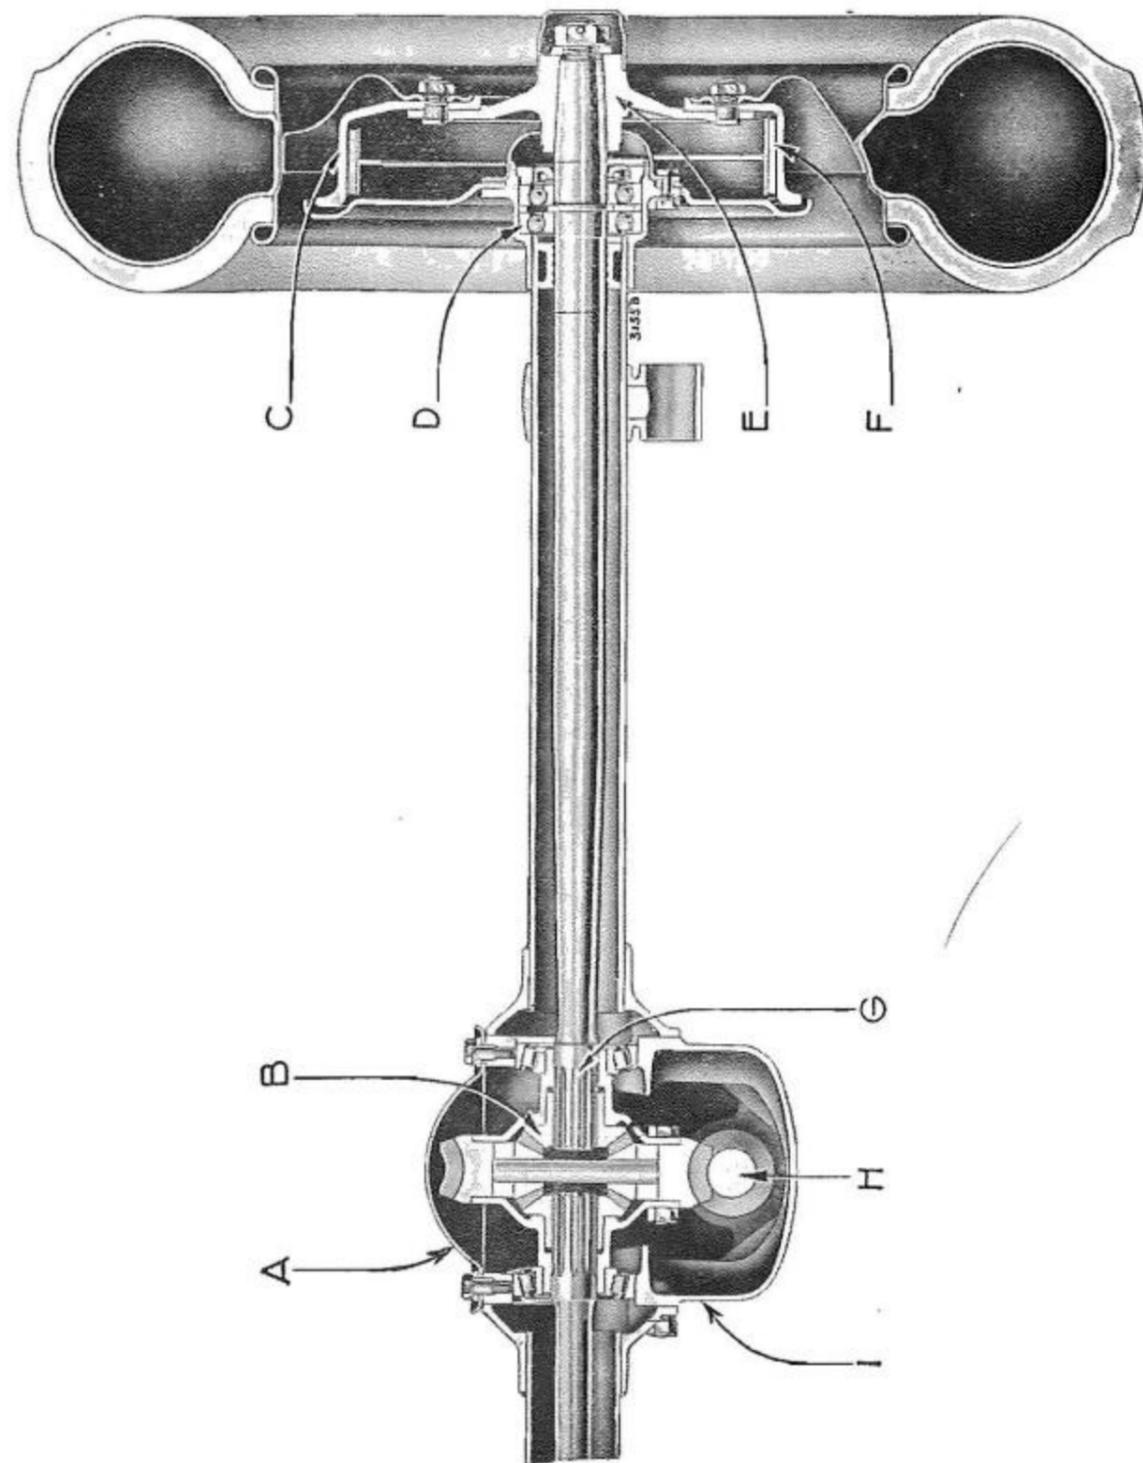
Coupe du pont arrière et d'une roue arrière.
